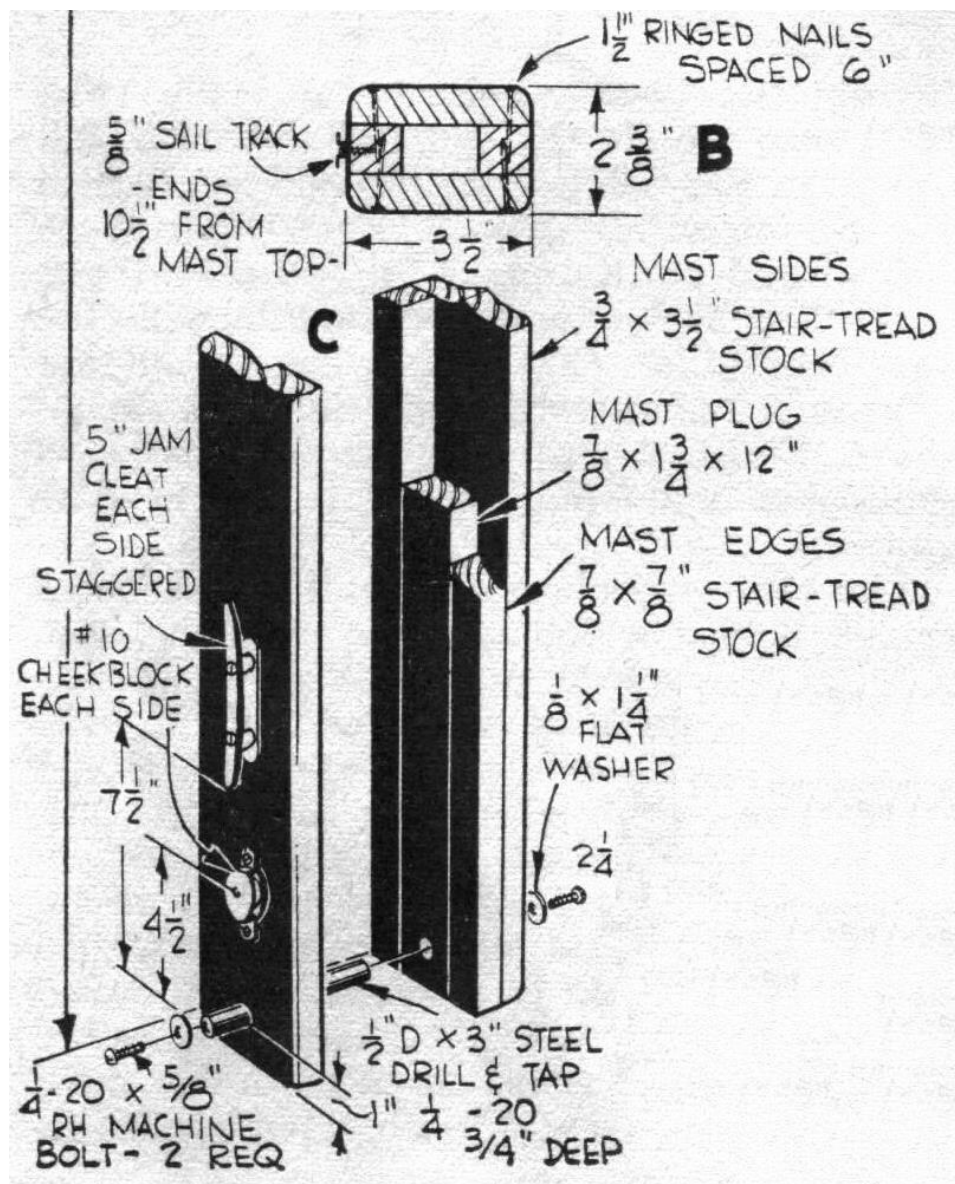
Plano mástil modelo original (Fuente: Svenson.com)
